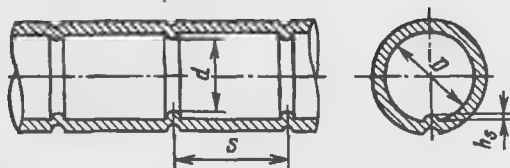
Общий вид трубы с поперечной кольцевой накаткой
